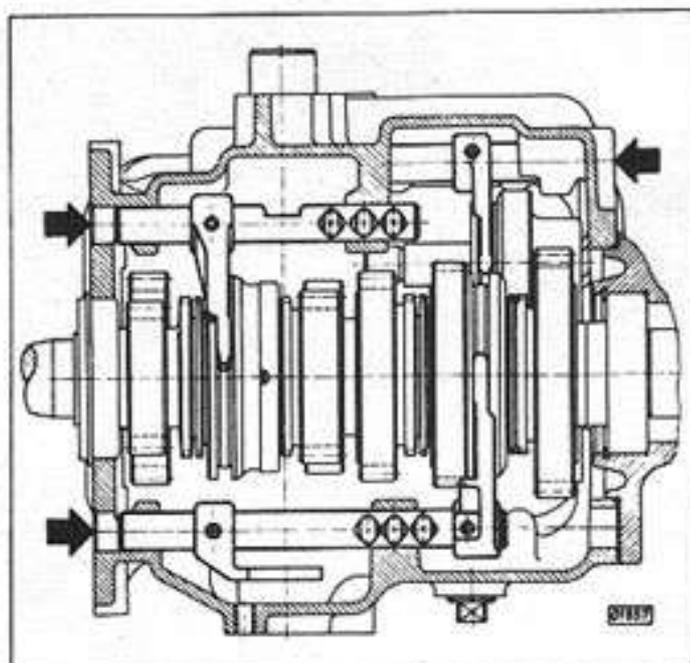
Montaje del eje selector del engranaje de marcha atrás y la horquilla selectora en la caja
